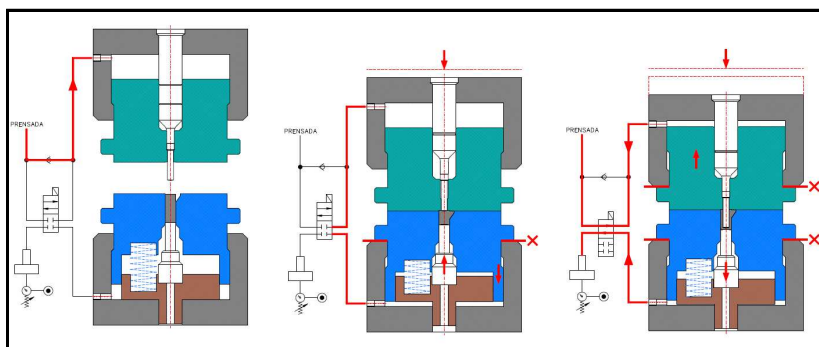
Prinzip der Werkzeugsystems mit hydraulischen Kissen
